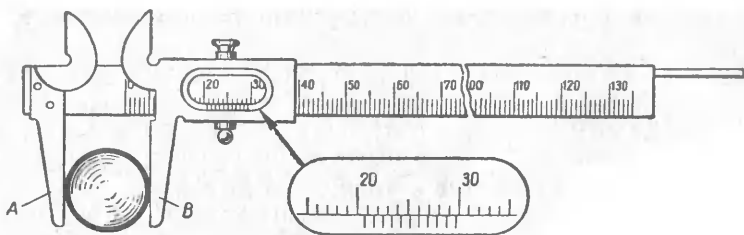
Измерение диаметра цилиндра штангенциркулем.
